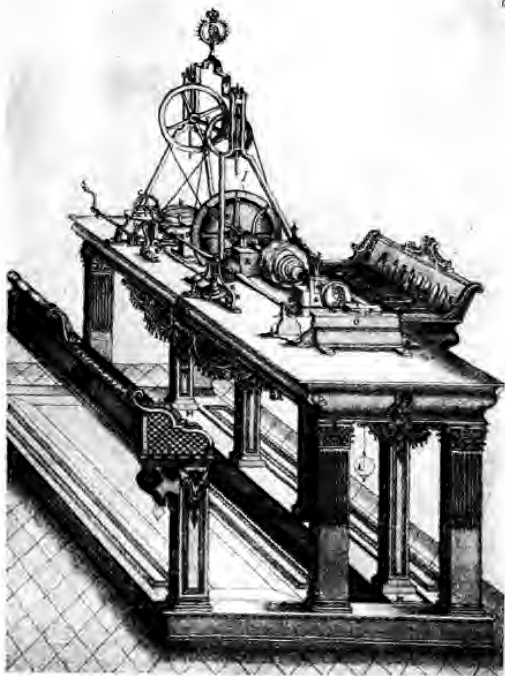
Токарно-копировальный станок для изготовления барельефов на плоскости и нанесения узоров. Ручпись «Театрум Махинарум» А. К. Нартова.
